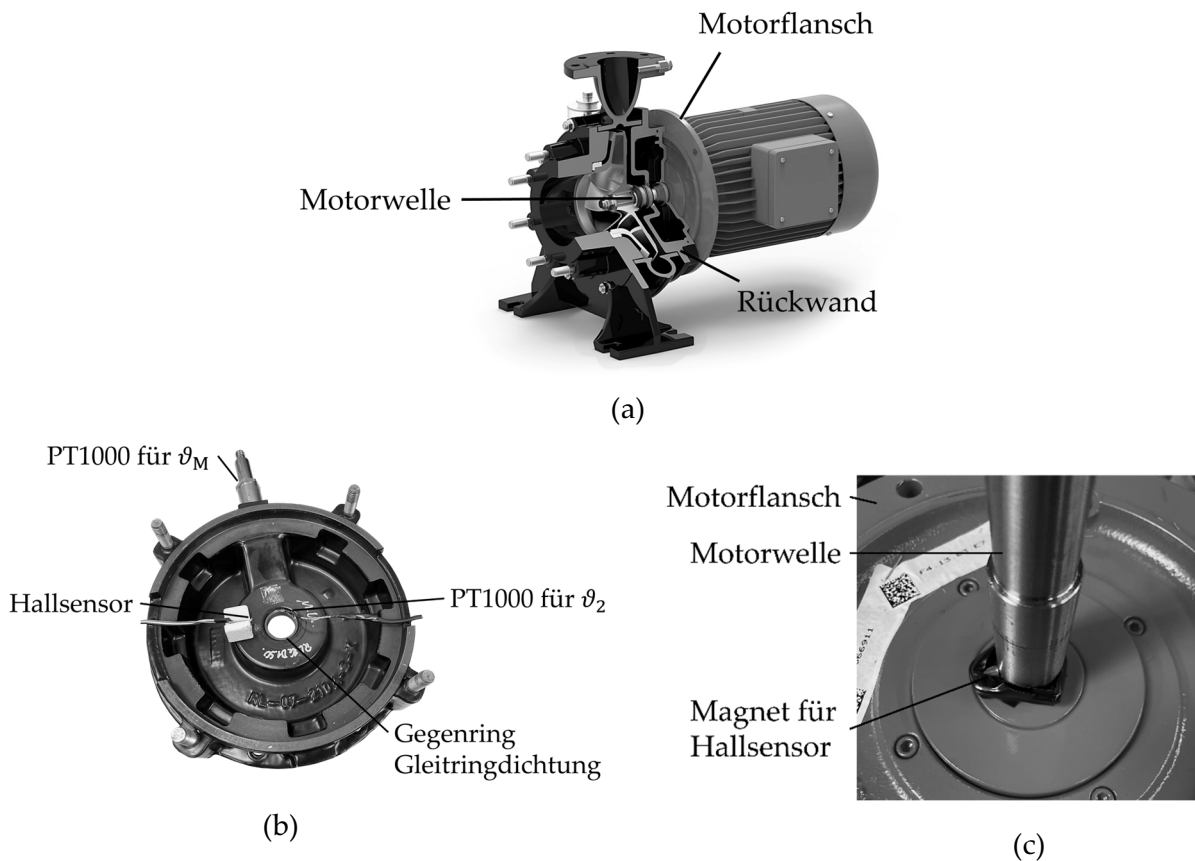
(a) Darstellung der Blockpumpenbauweise mit Bezeichnung der Motorwelle, des Motorflansches und der Rückwand der Pumpe. (b) Ansicht der Rückwand aus Richtung des Motorflansches mit Bezeichnung des PT1000 zur Messung von  $\vartheta_M$ , des PT1000 am Gegenring der Gleitringdichtung zur Messung von  $\vartheta_2$  und des Hallensensors zur Messung von  $n$ . (c) Ansicht auf den Motorflansch aus Richtung der Rückwand mit Bezeichnung der Motorwelle und des an dieser befestigten Magneten für die Drehzahlmessung durch den Hallensensor.
